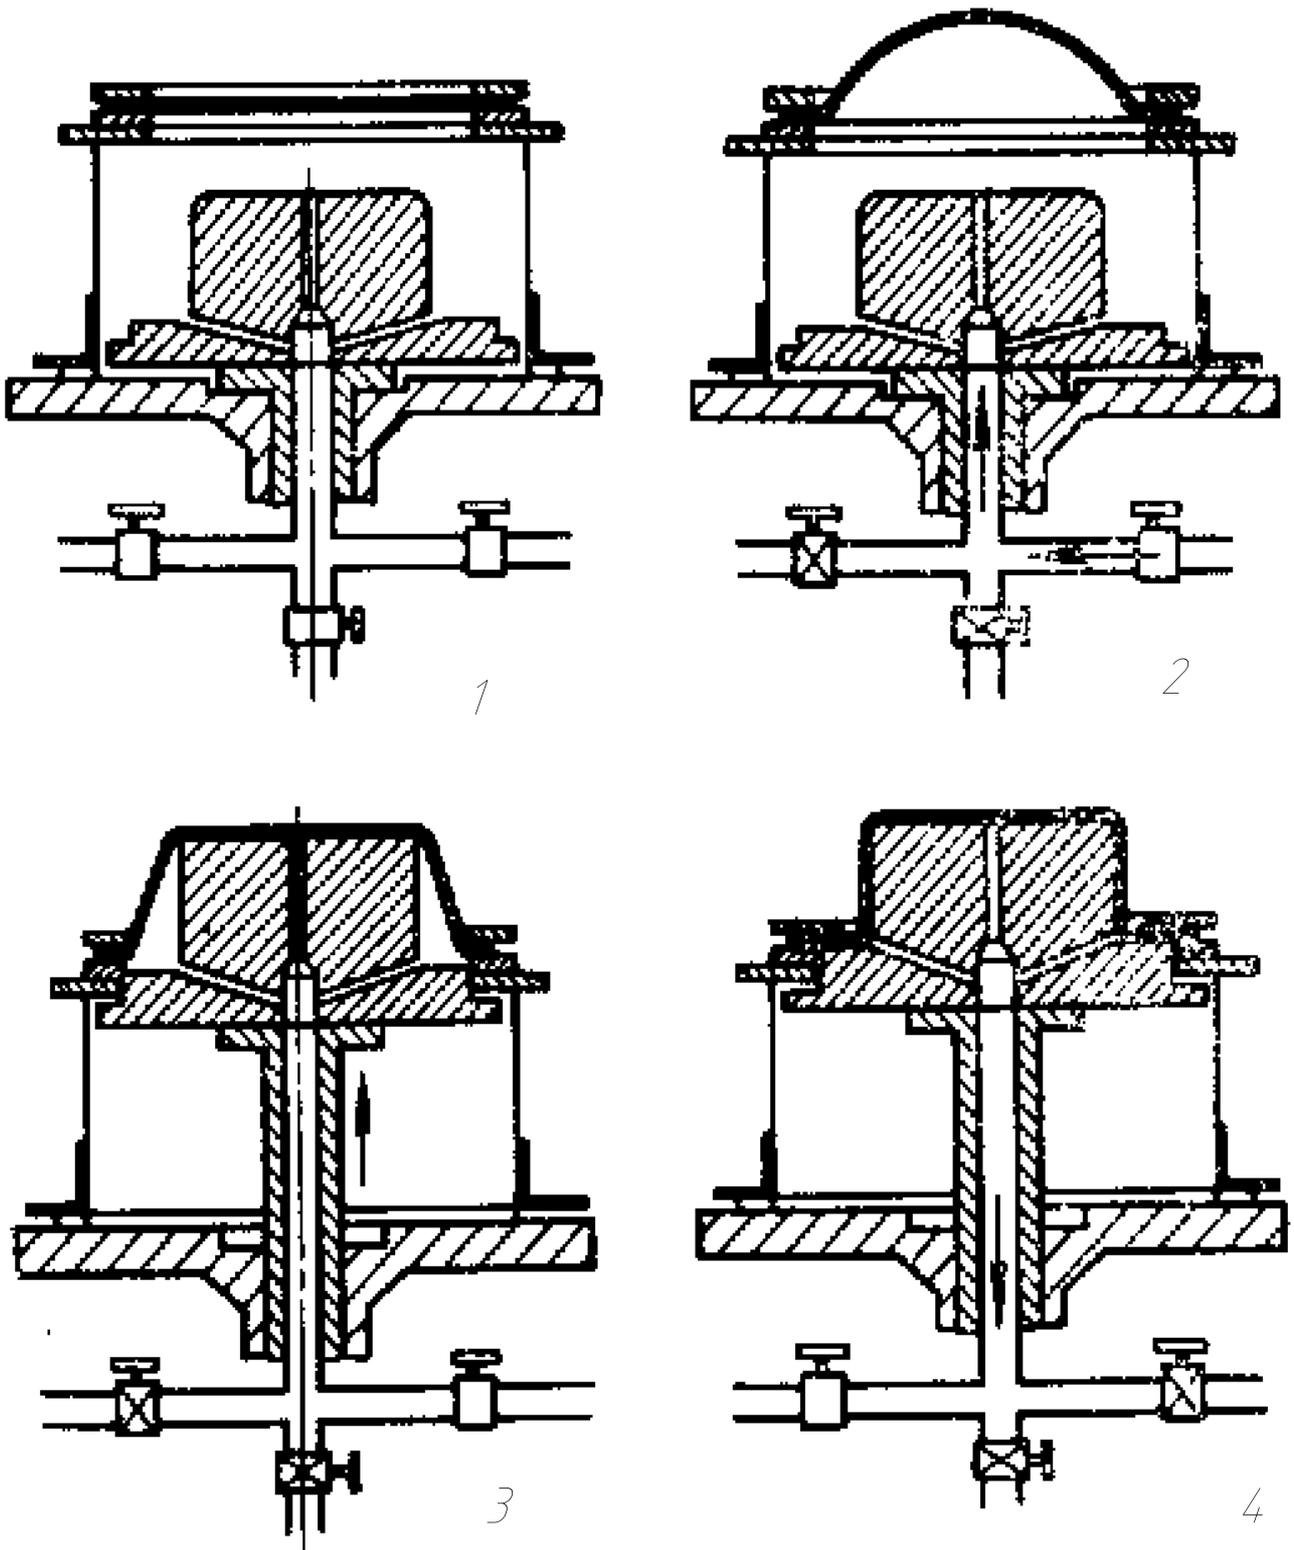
Конструкция для вакуумного позитивного способа полых деталей из листовых термопластов.
